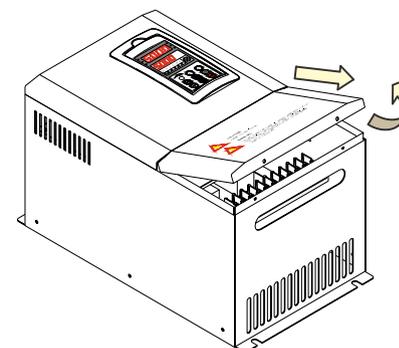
Демонтаж верхней крышки инвертора типа В
